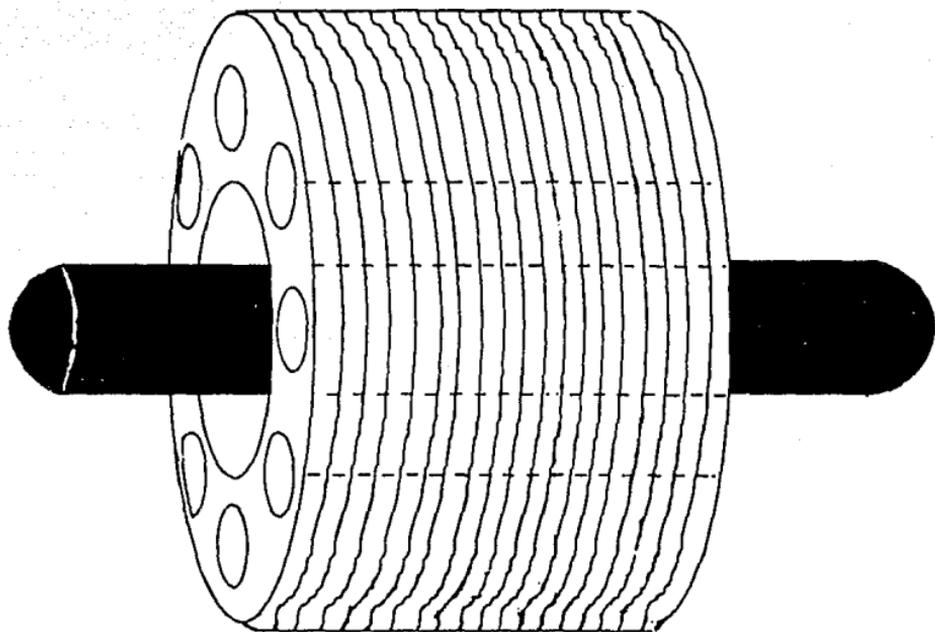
Rotor de un motor de Jaua de Ardiã
